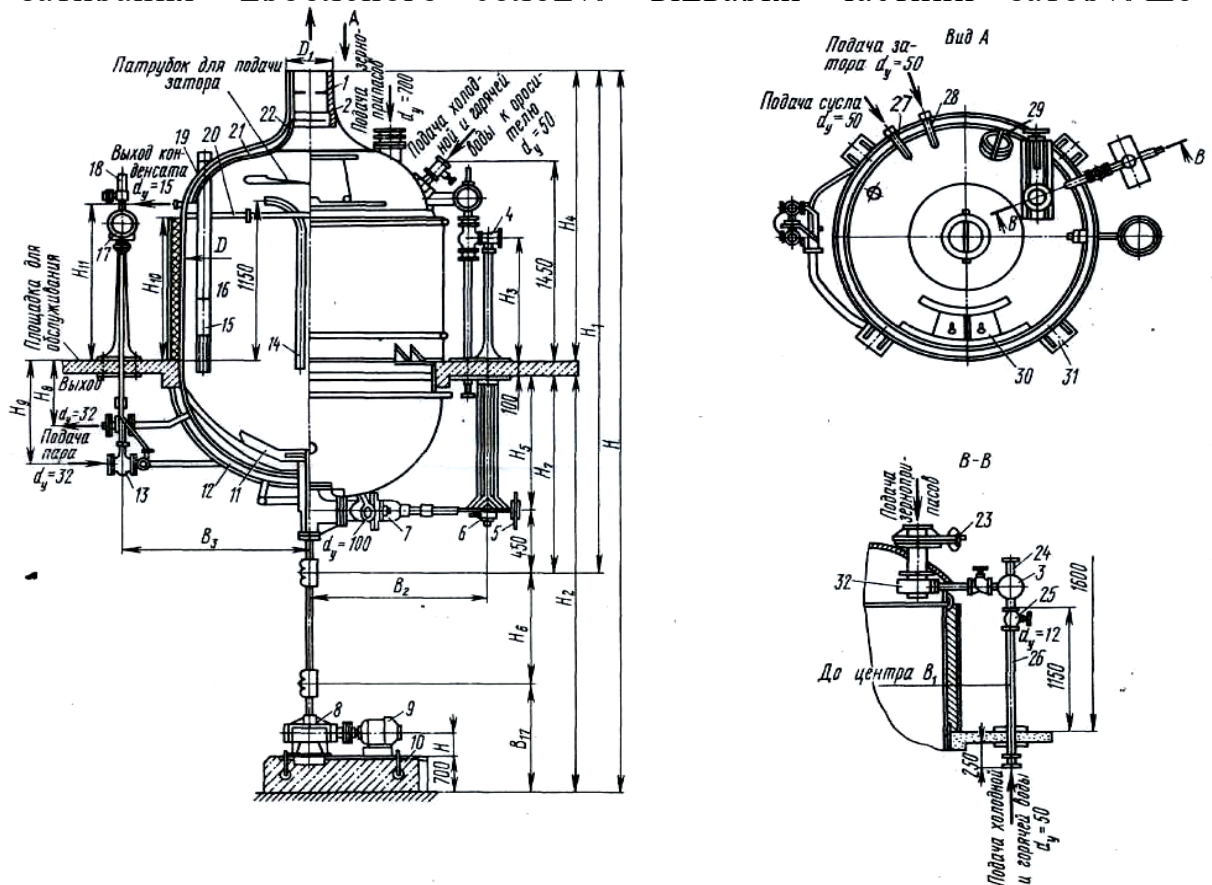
4. Заторно-сусловарильний казан ВСЦ-1: 1 - дросельна заслінка; 2 - витяжна труба; 3 - змішувач; 4 - патрубок; 5 - маховички для керування розвантажувальним пристроєм; 6 - конічна зубчаста передача; 7 - розвантажувальний пристрій; 8 - черв'ячний редуктор; 9 - електродвигун; 10 - фундамент; 11 - пропелерна мішалка; 12 - подвійне сферичне днище; 13 - вентиль для подачі пари; 14 - труба патрубка для подачі сусла; 15 - мірна лінійка; 16 - сталевий циліндричний резервуар; 17 - маховичок (рукоятка керування); 18 - манометр; 19-сферична кришка; 20 - трубчастий зрошувач; 21 - труба для відводу конденсату; 22 - кільцевий збірник конденсату; 23 - шиберна засівка; 24 - термометр; 25 - труба для води; 26 - штуцер; 27 - патрубок для подачі
